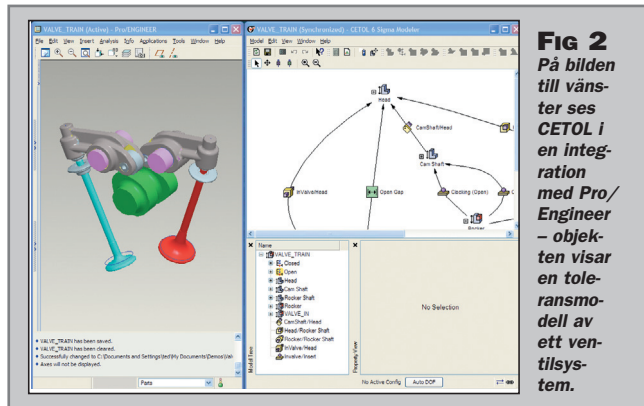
På bilden till vänster ses CETOL i en integration med Pro/Engineer - objektet visar en toleransmodell av ett ventilsystem.
